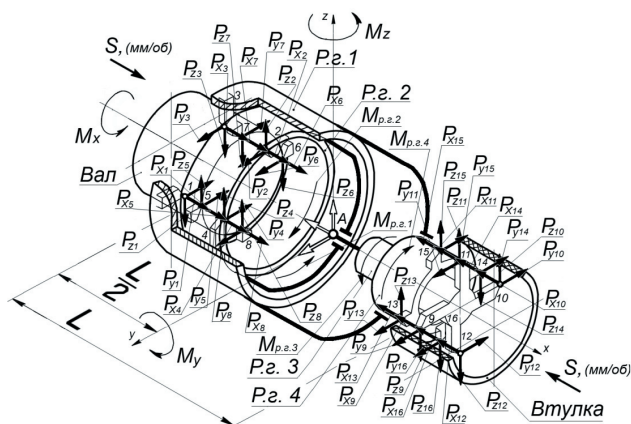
Розрахункова схема механічної обробки сполучуваних поверхонь деталей (вал, втулка) із ПКМ при виготовленні циліндричної посадки
